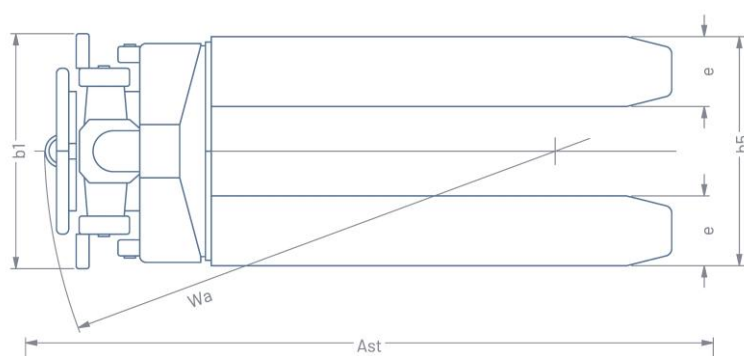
ZAC-S &amp; ZAC-E Draufsicht mit Kürzeln
